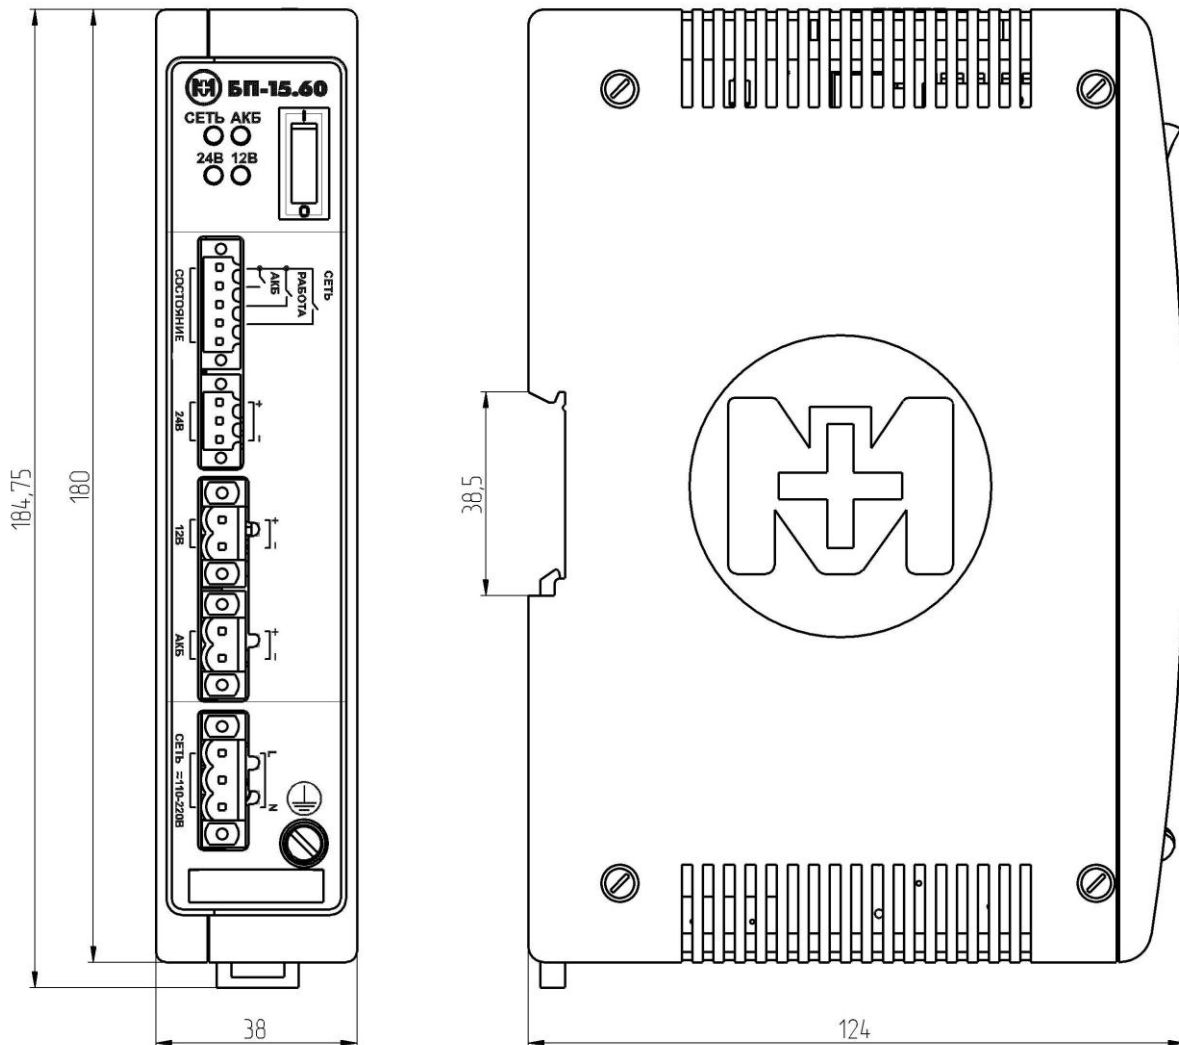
Габаритные размеры блока БП-15.60
